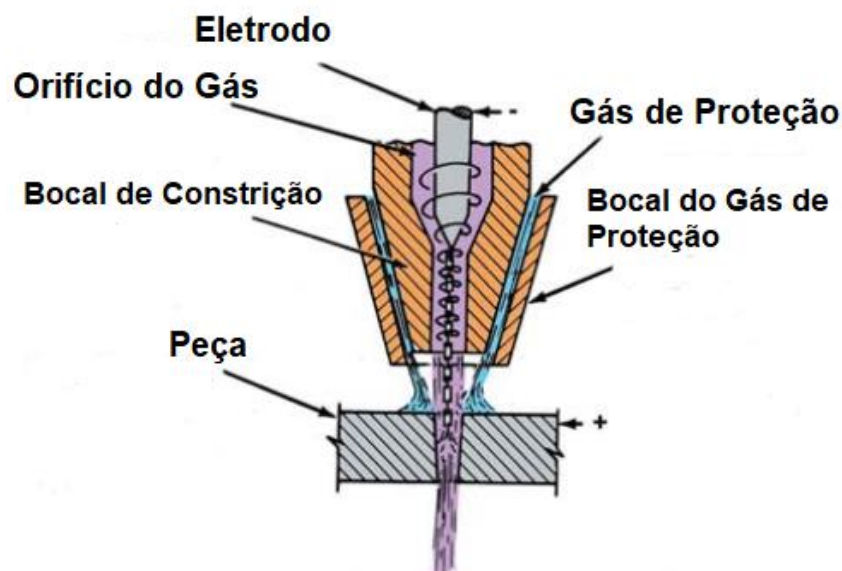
Bocal de corte a plasma (Traduzido de Weld Handbook, 2001)
